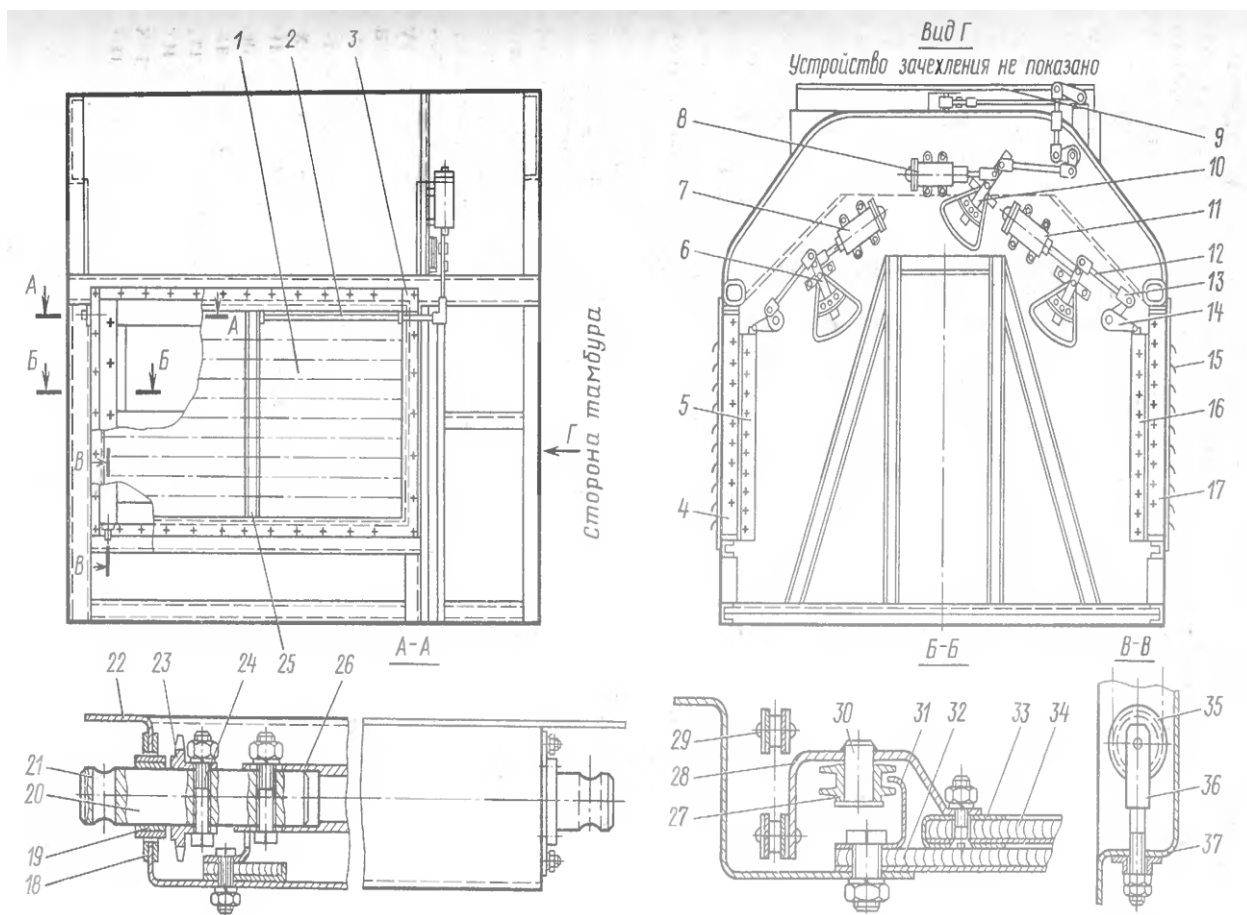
Боковые и верхние жалюзи холодильной камеры, устройство зачехления жалюзи:
